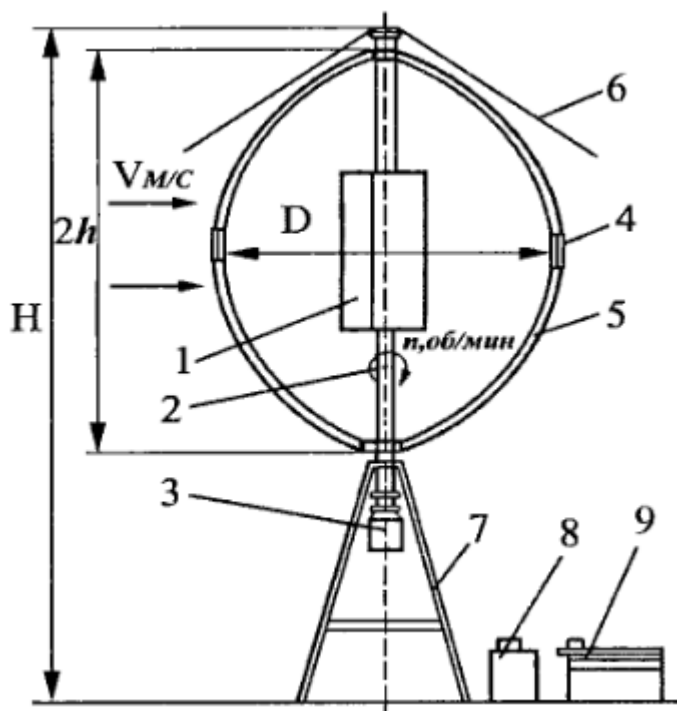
Конструктивна схема ВЕУ з вертикальною віссю обертання: 1 – стартер (ротор Савоніуса); 2 – вал; 3 – електрогенератор; 4 – тормозний пристрій; 5 – робоча лопать; 6 – розтяжки; 7 – рама; 8 – перетворювач енергії; 9 – акумулятор.
